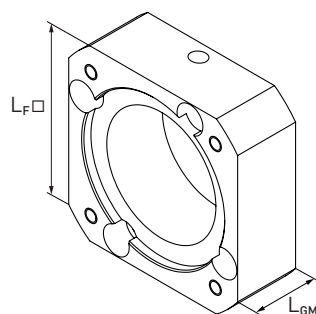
Motorgetriebeadapterplatte GM für Linearmodule HM-B, Lineartische HT-B und Auslegerachsen HC
